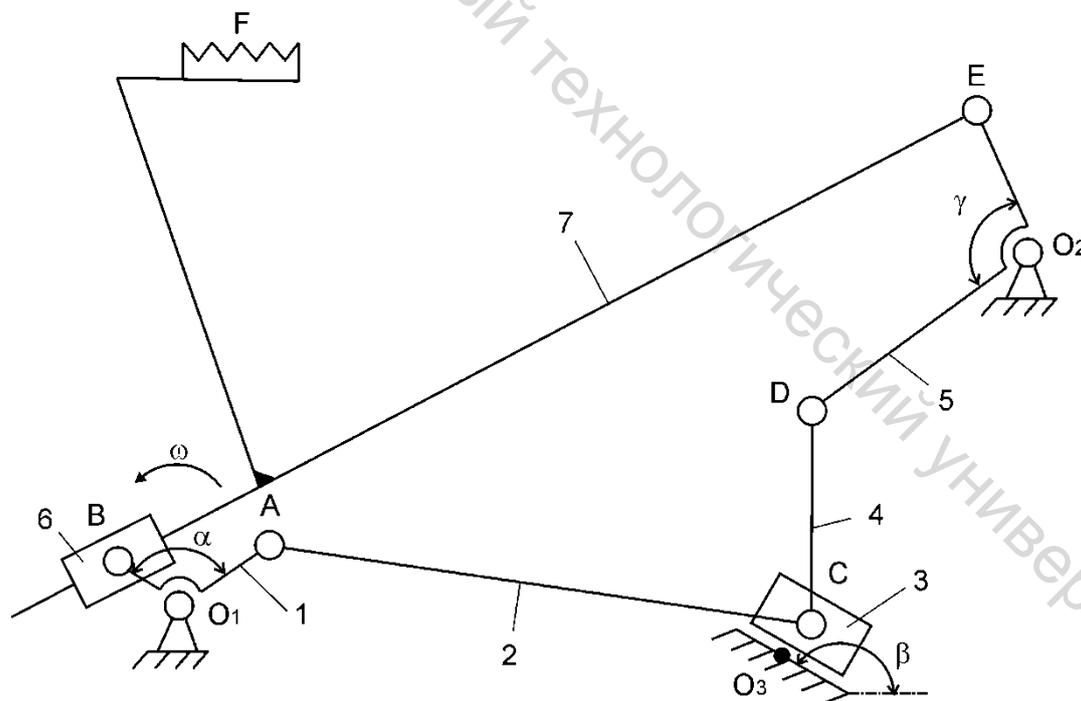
Кинематическая схема механизма рейки машины GC-20606 Typical
